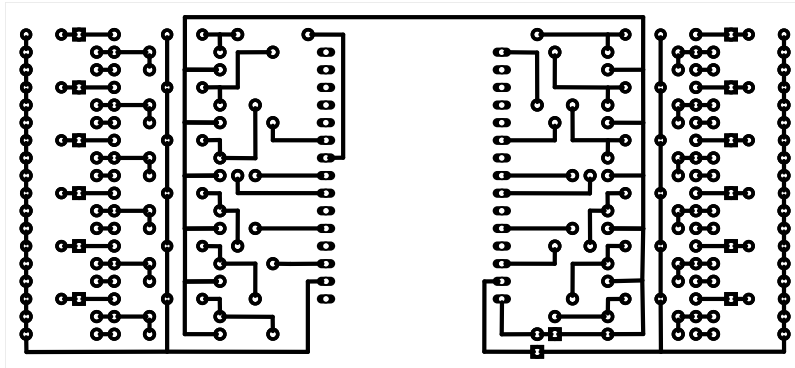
PCB do projeto com 12 *drivers*, 6 de cada lado da placa
